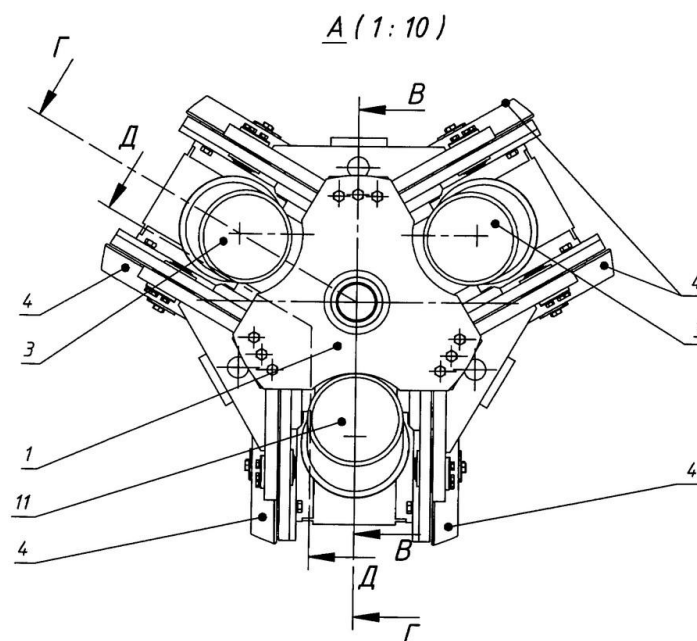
Механизм перемещения машины для сварки труб, в дальнейшем "механизм перемещения", вид А
